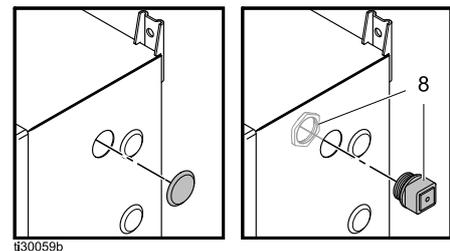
Drehzahlreglerstecker, Kabelfitting und Mutter
